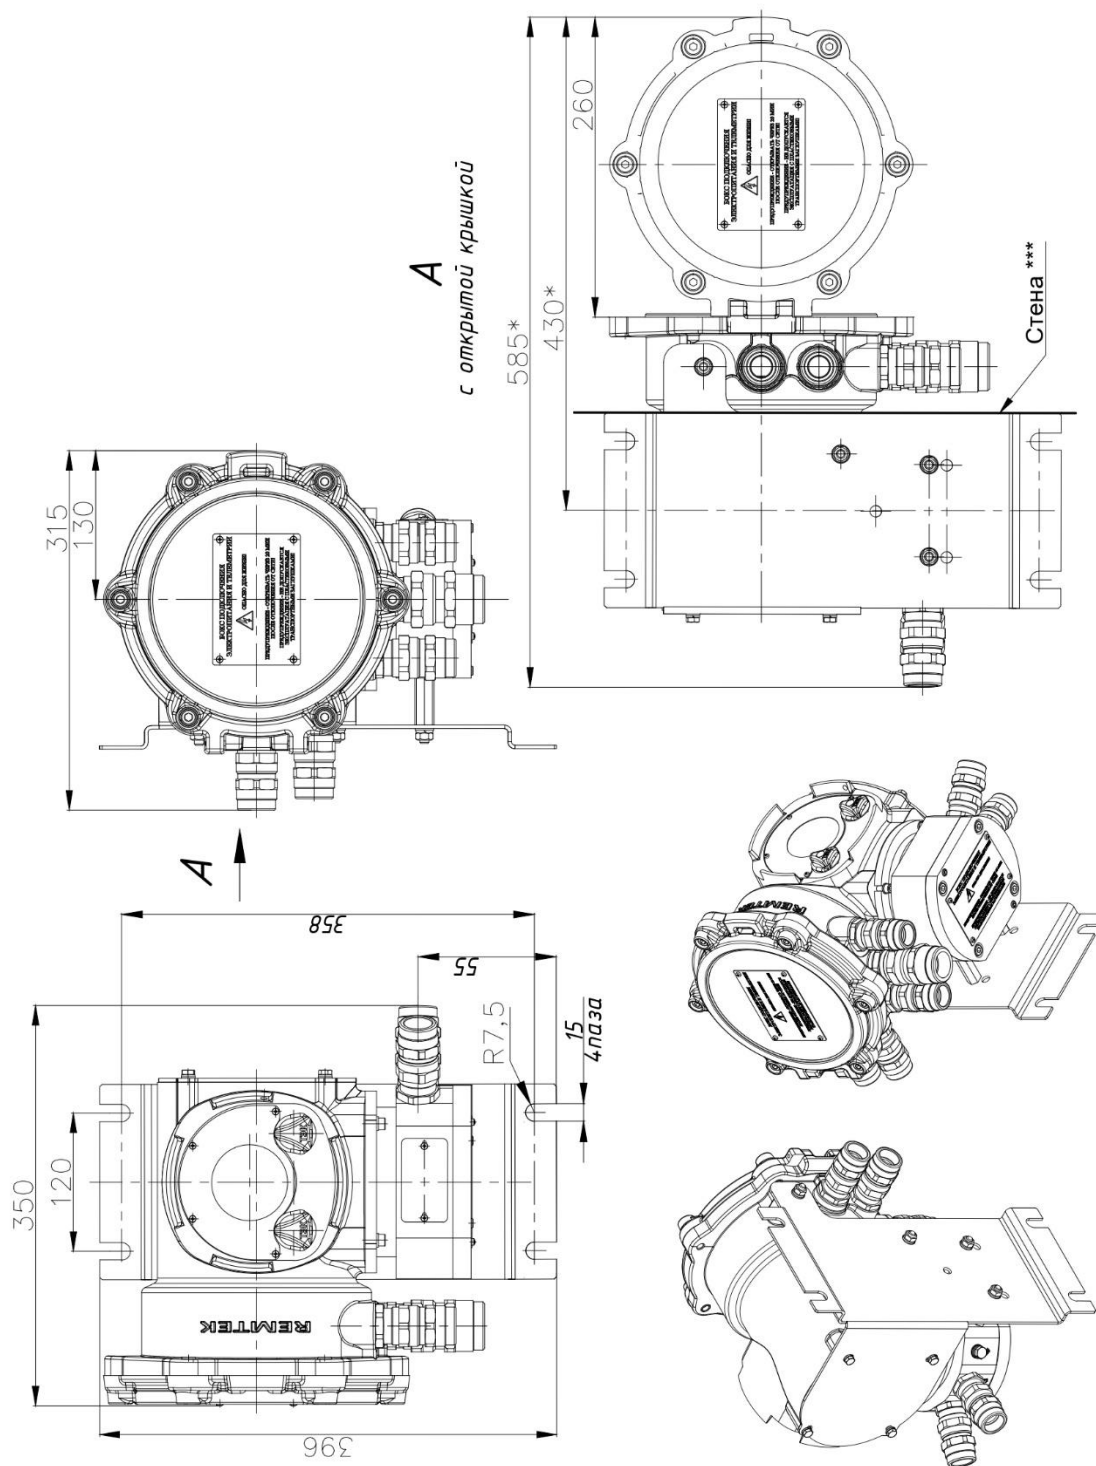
Внешний вид и габаритные размеры ВБУ
